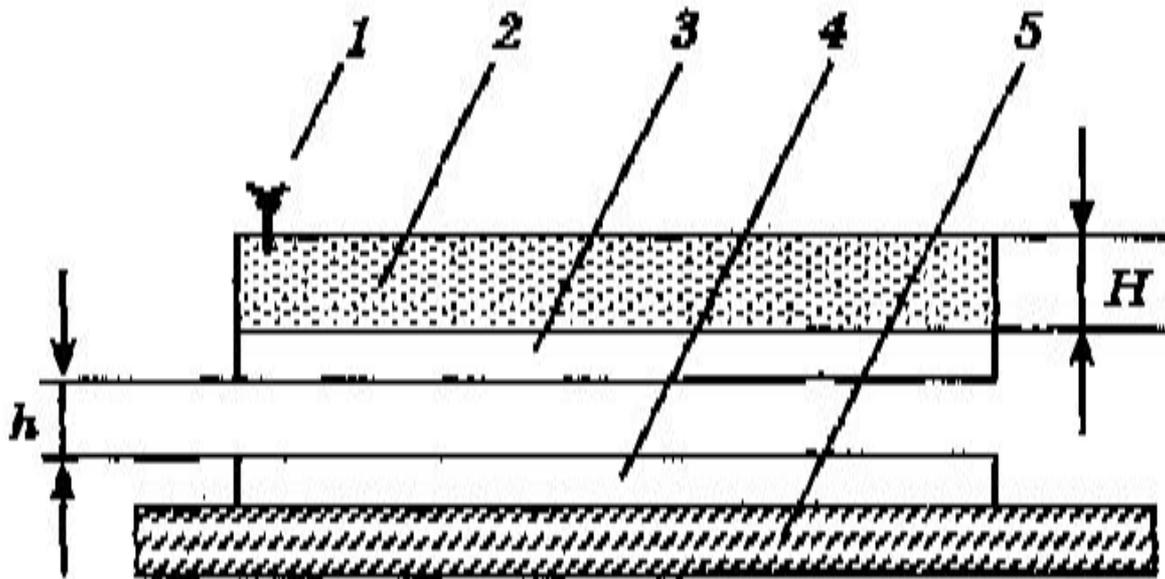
Схема сварки взрывом с параллельным расположением пластин
